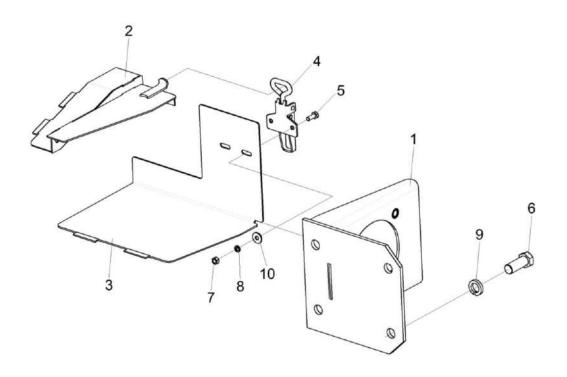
Установка привода жатки ЖКС-45-0100170
